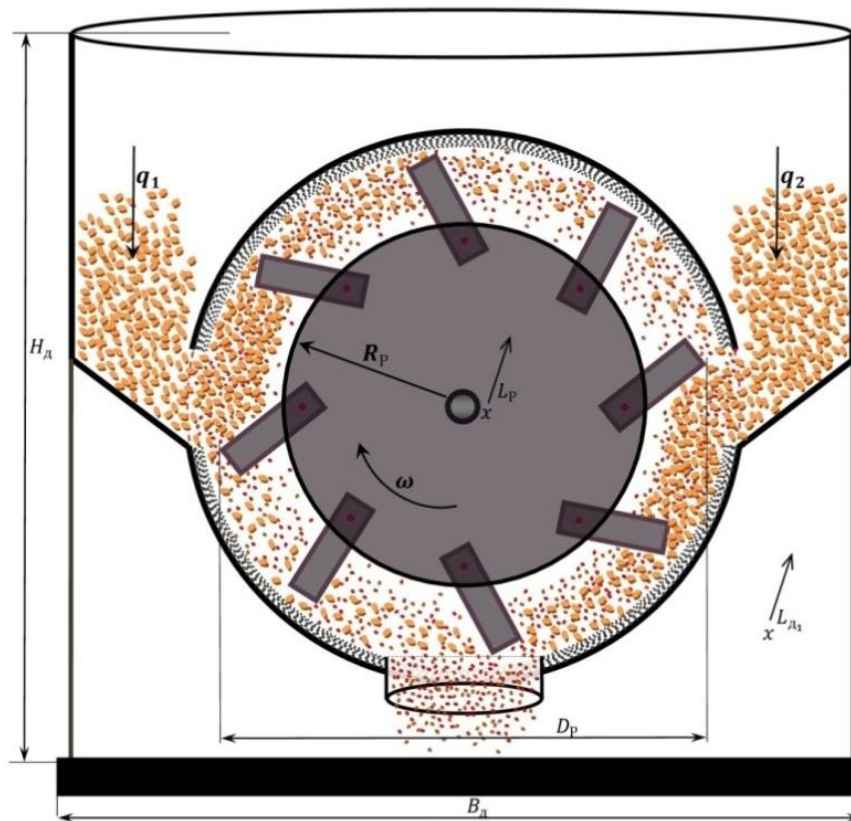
Схема зернодробилки с оппозитной загрузкой
